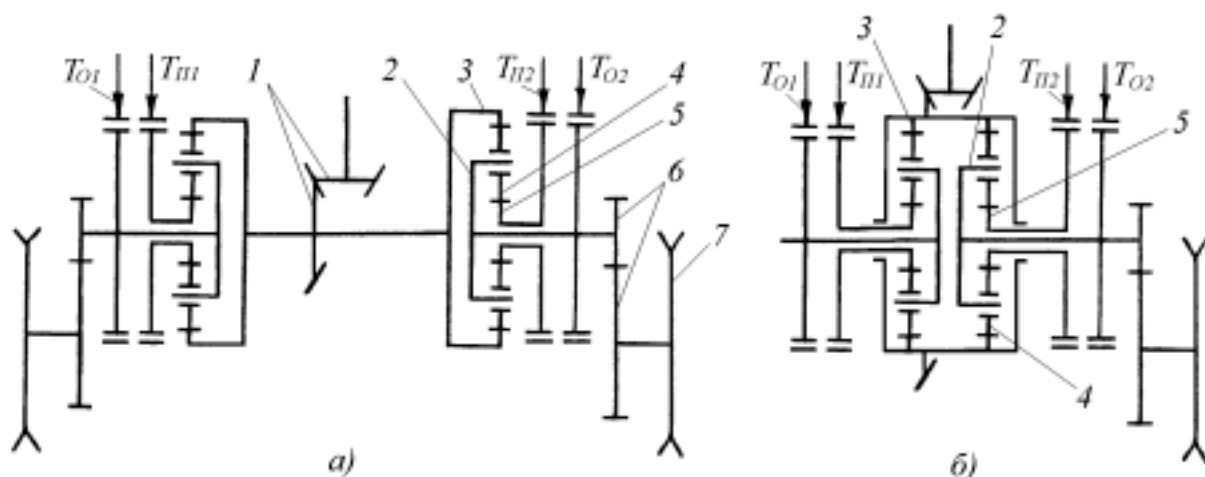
Одноступенчатый планетарный механизм поворота:
